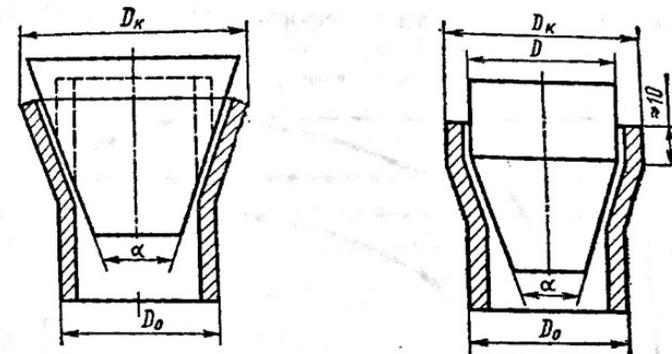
Схема испытания патрубков на раздачу траверсы машины Р-20 (рис.3). Размеры патрубка определяются п. 2.1. ГОСТ 8694. Рабочая поверхность оправки (конуса) должна иметь твердость $\text{HRC} \geq 50$. Скорость внедрения оправки в патрубок должна быть $20...50$ мм/мин. Величина раздачи вычисляется в процентах: $X = (D_k - D_0) / D_0 / 100$ и составляет $(10...20)\%$. Трещины и надрывы на внешней и внутренней поверхностях патрубка не допускаются.
